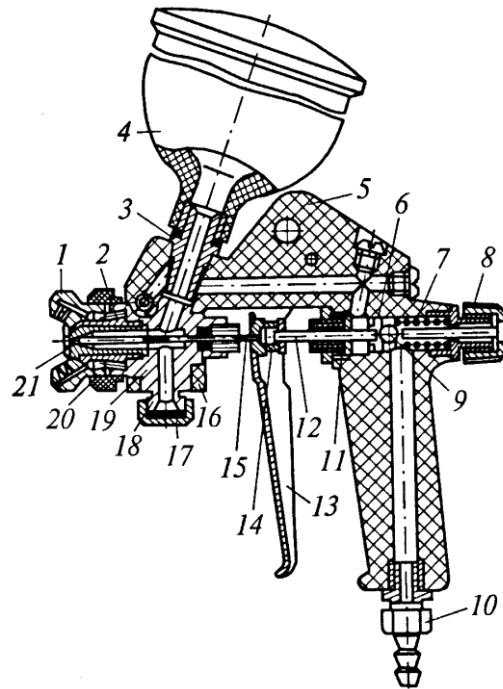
Фарборозпилювач КРУ-1 с верхнім розташуванням бачка:
